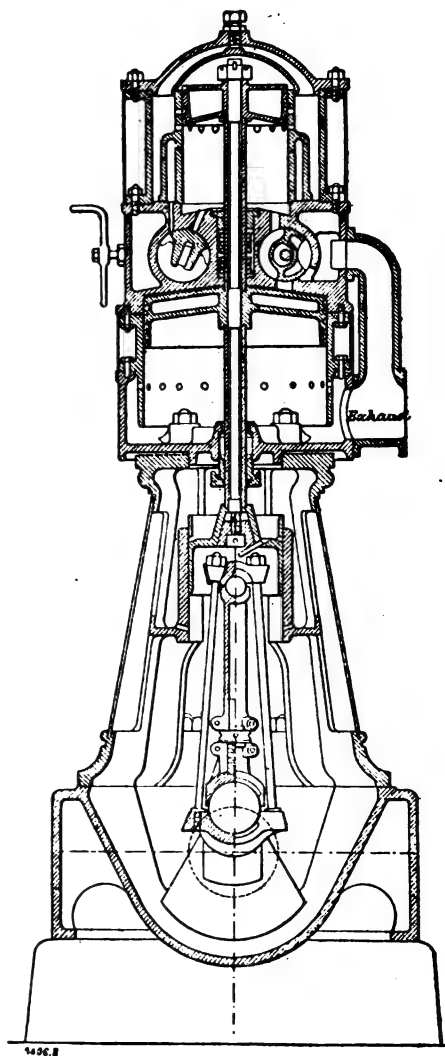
Coupe faite par un plan vertical normal au premier.
